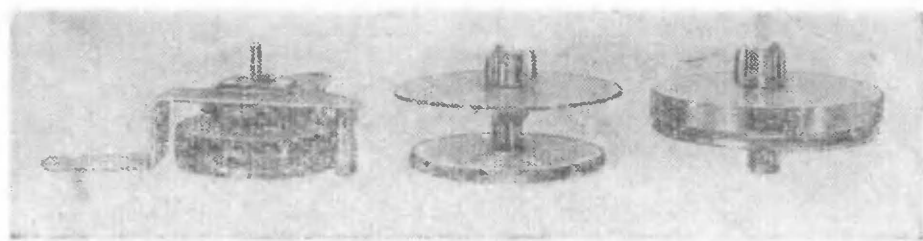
Внешний вид узла ведущего вала (слева) и подгательников подающего и приемного узлов
